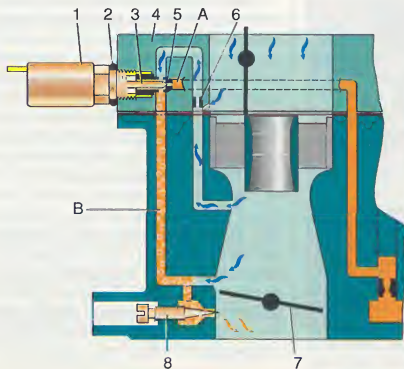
Фрагмент системы холостого хода: 1 — электромагнитный клапан; 2 — прокладка; 3 — игла; 4 — корпус; 5 — топливный жиклер; 6 — воздушный жиклер; 7 — дроссельная заслонка; 8 — винт качества; А и В — каналы.
